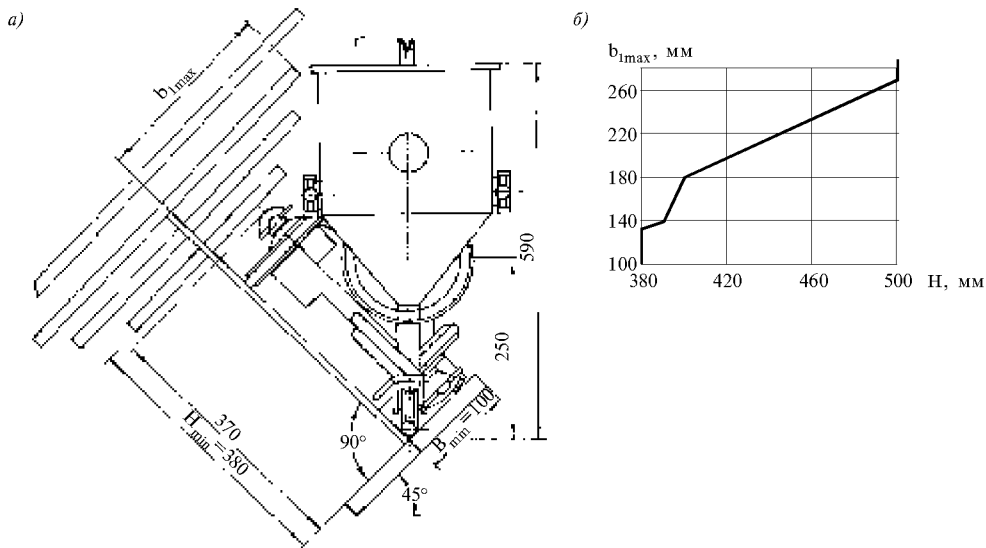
Доступность наложения швов при автоматической сварке балок в положении «в лодочку»
